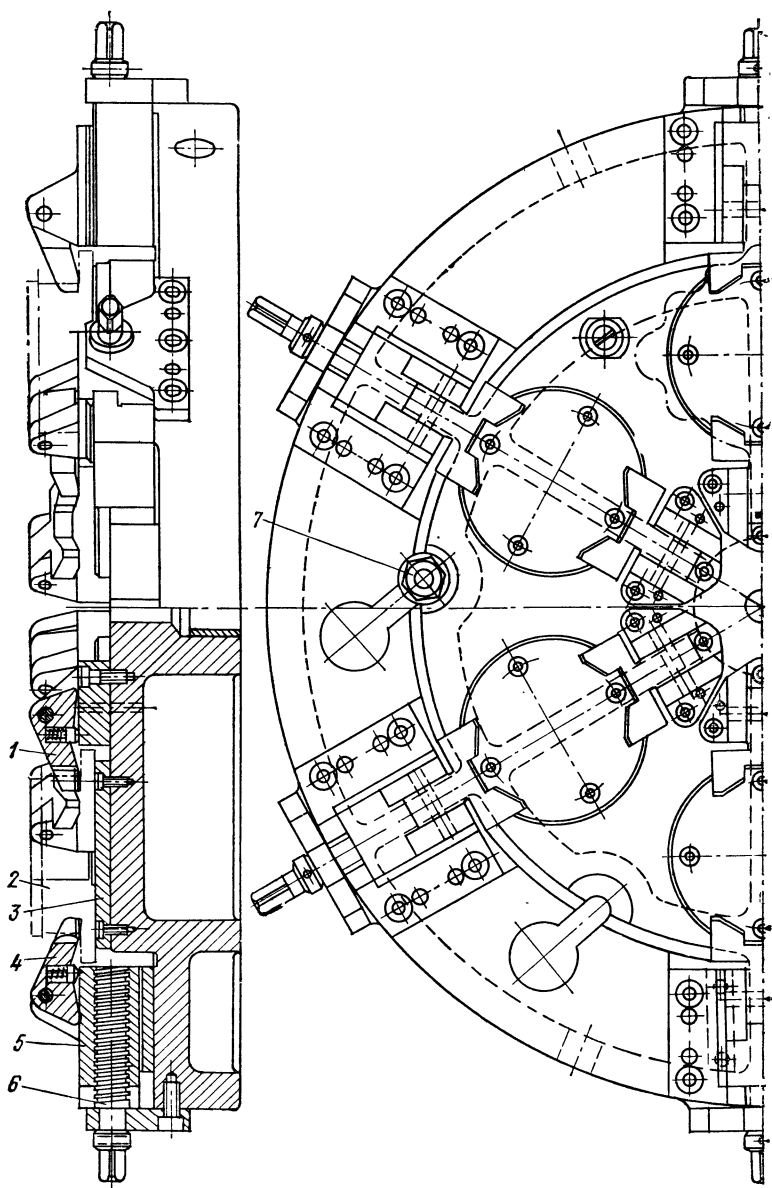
Многочастная наладка при обработке корпусов методом непрерывного фрезерования
